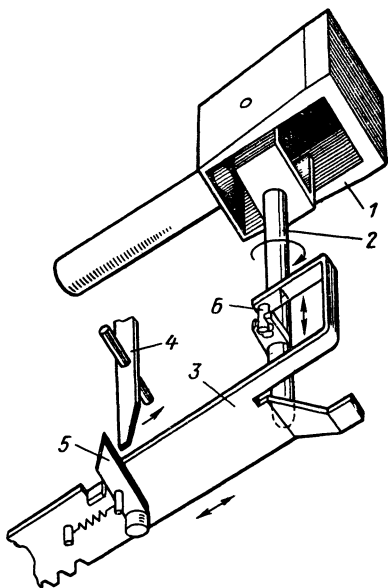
Командный механизм, управляемый зубчатой рейкой.
